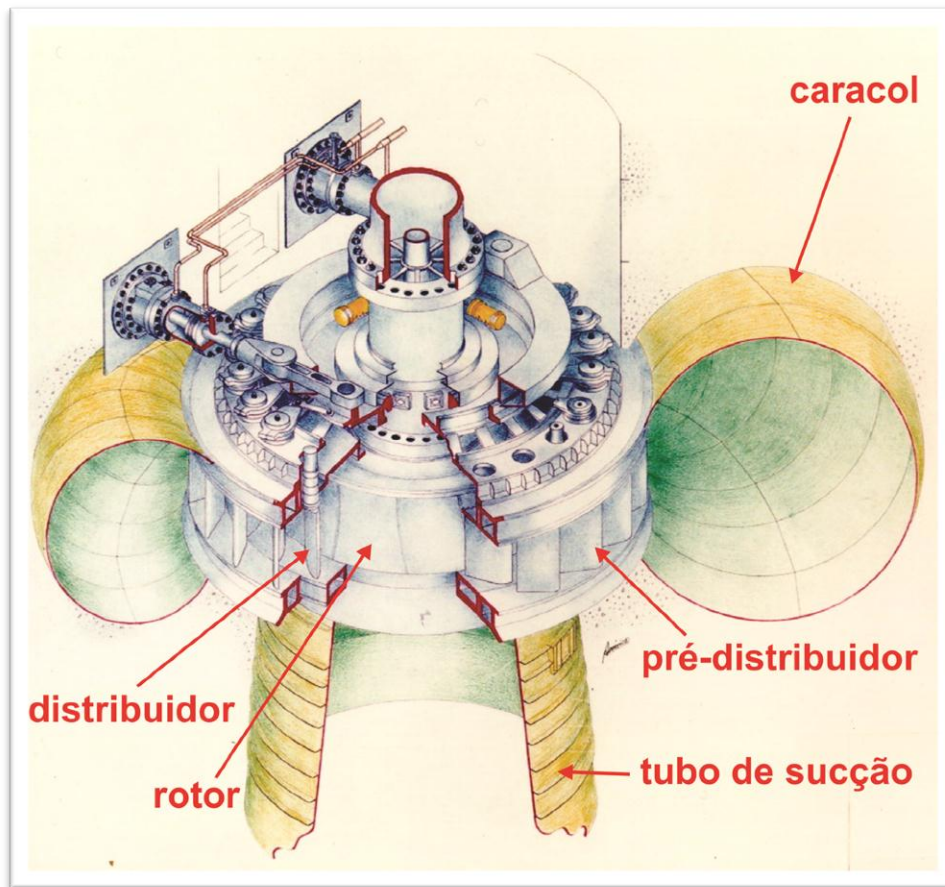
Turbina Hidráulica Francis com sistema mecânico e hidráulico adaptada de www.itaipu.gov.br.
